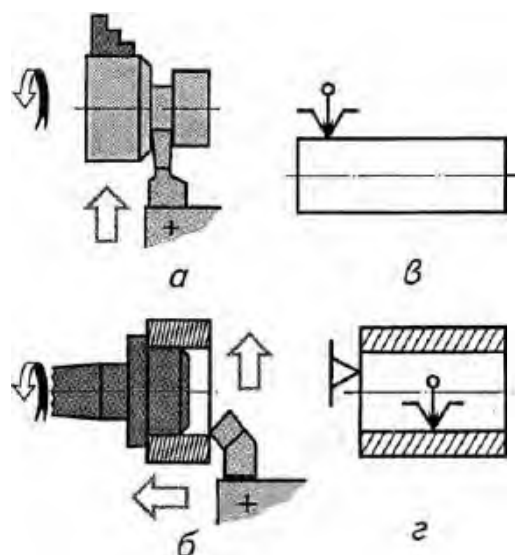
СХЕМИ БАЗУВАННЯ ЗАГОТОВКИ ПО ПОВЕРХНЯХ
